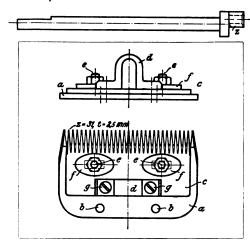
Kurbelstück der Schermaschine. Fig. 2 und 3. Maschinenschere. a Grundplatte mit Befestigungsschrauben h.h. c bewegte Platte mit Führungsbügel d für den Kurbelzapfen 2, c.e. Führungsbülzen. // Druckplatten.
